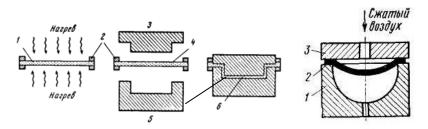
Схема процесса прессформования (a) и пневмоформования (б) изделия из термопластичной листовой заготовки [19]:
